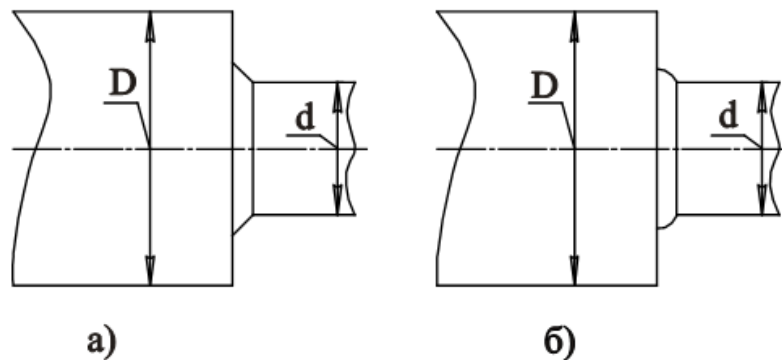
Варіанти виконання вставок поршневих дозувальних пристроїв: а - з фаскою при вершині; б - з випуклим заокругленням при вершині; 1 – мірний циліндр; 2 – вставка.
